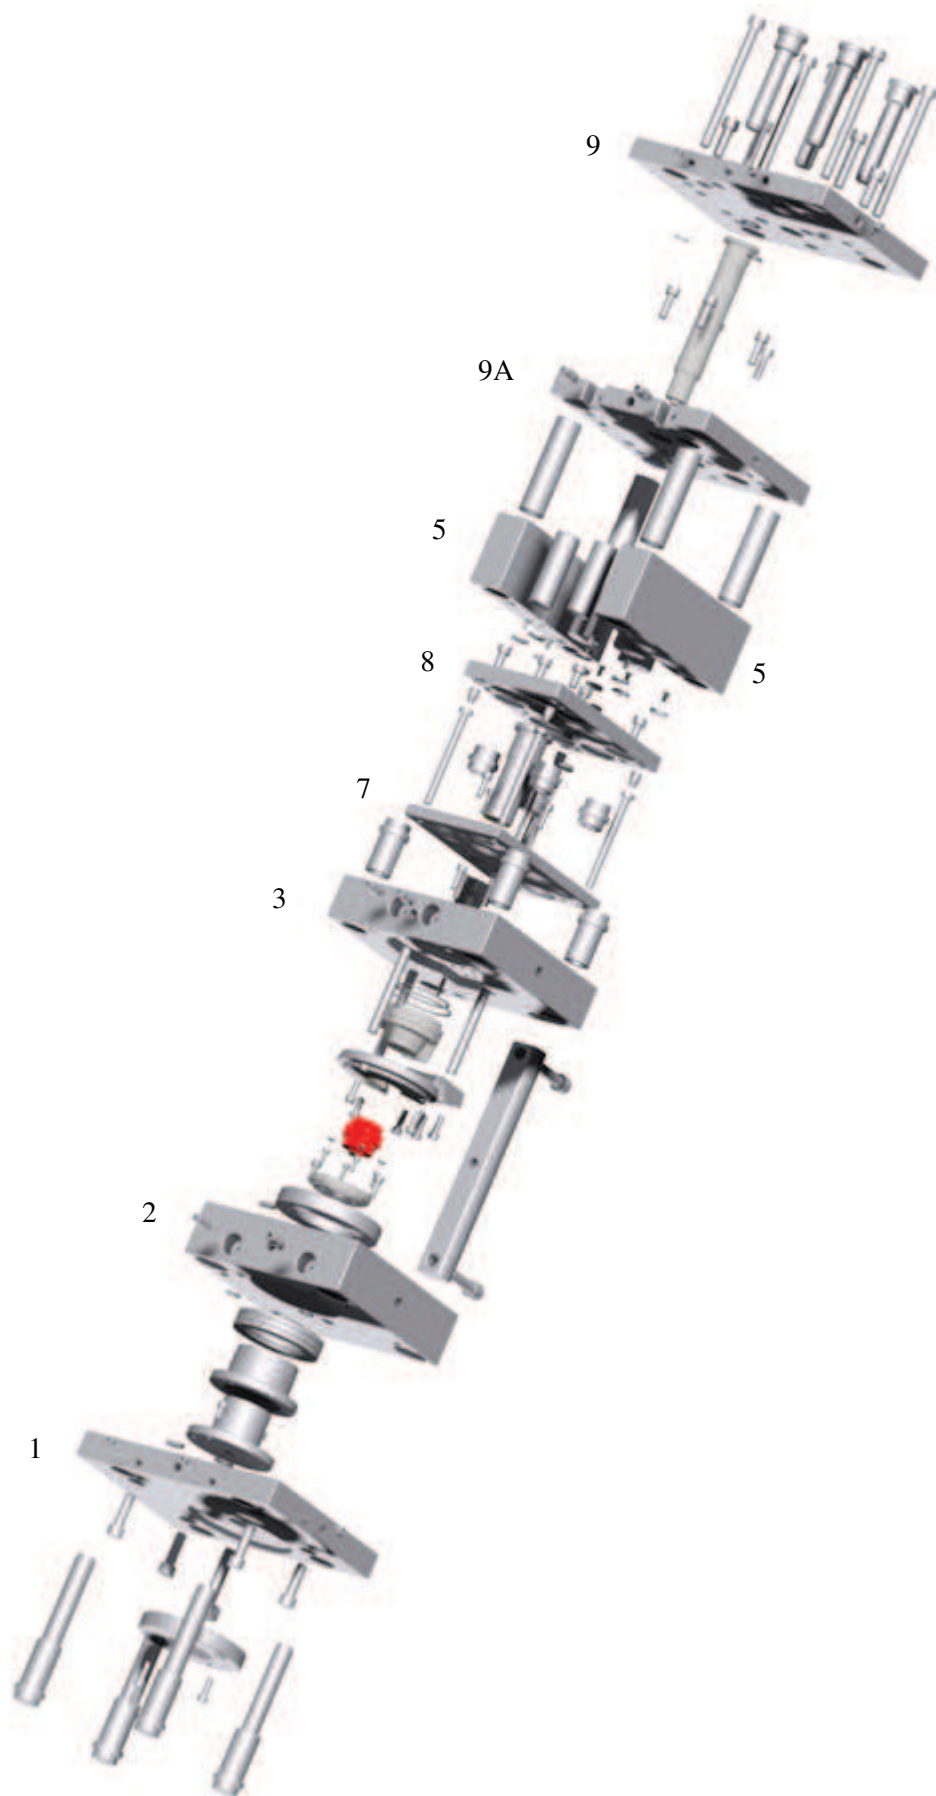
Vista global molde de injeção (827): lado injeção e lado da extração.
